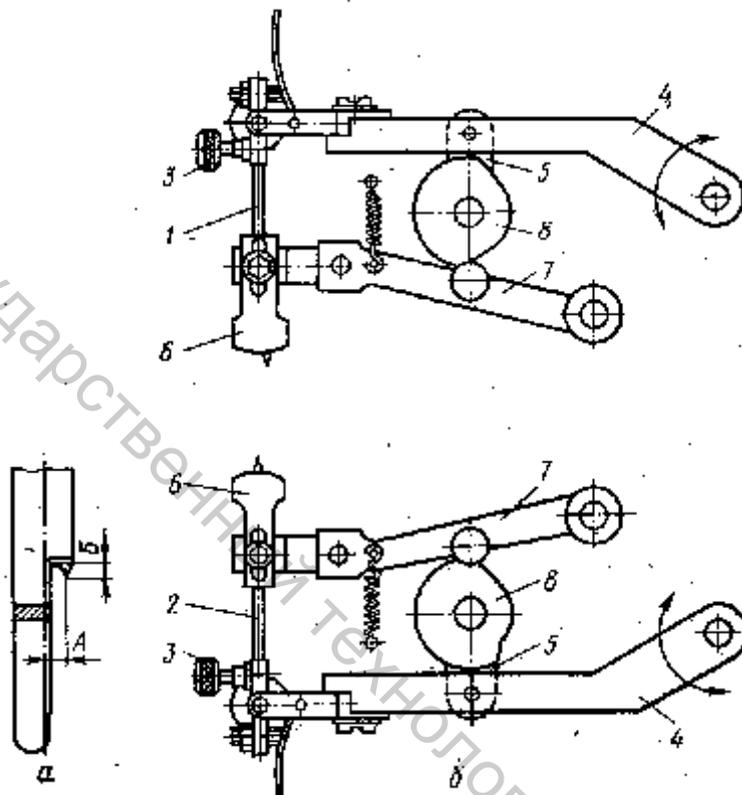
Отборная игла (а) и схема механизма отбора нитей (б)
